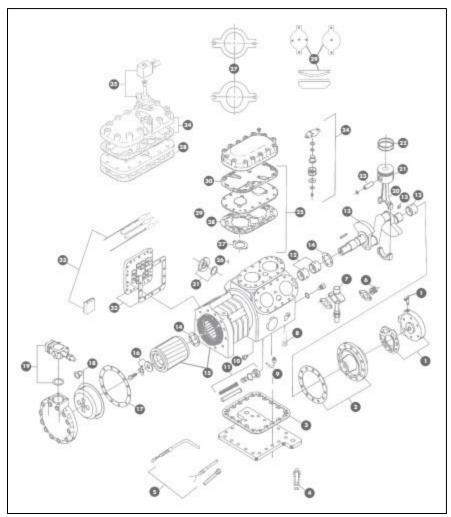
Despiece de Copeland típico 6D Fuente: (Copeland)
